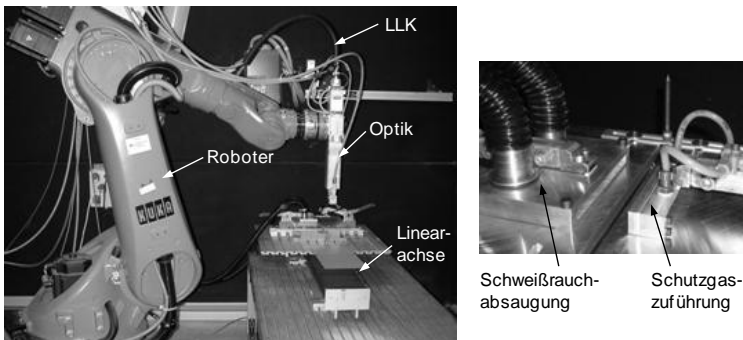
Versuchsaufbau (links) mit Spannvorrichtung und integriertem Schutzgaszuführ- und Schweißrauchabsaugsystem (rechts)
